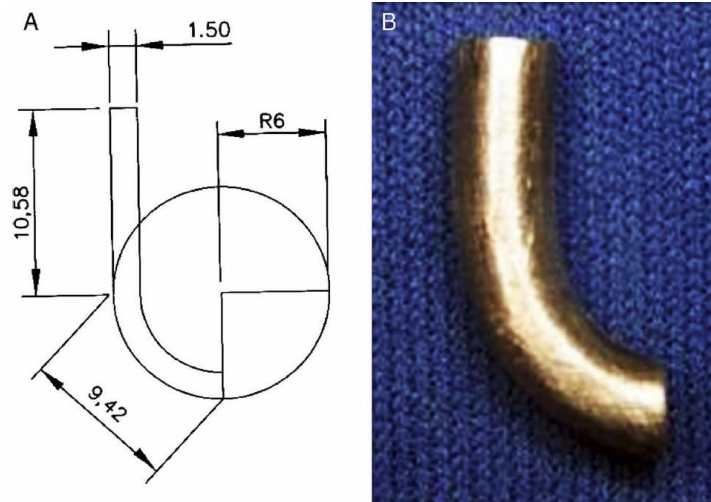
Dimensões e características geométricas do canal artificial produzido [6].
